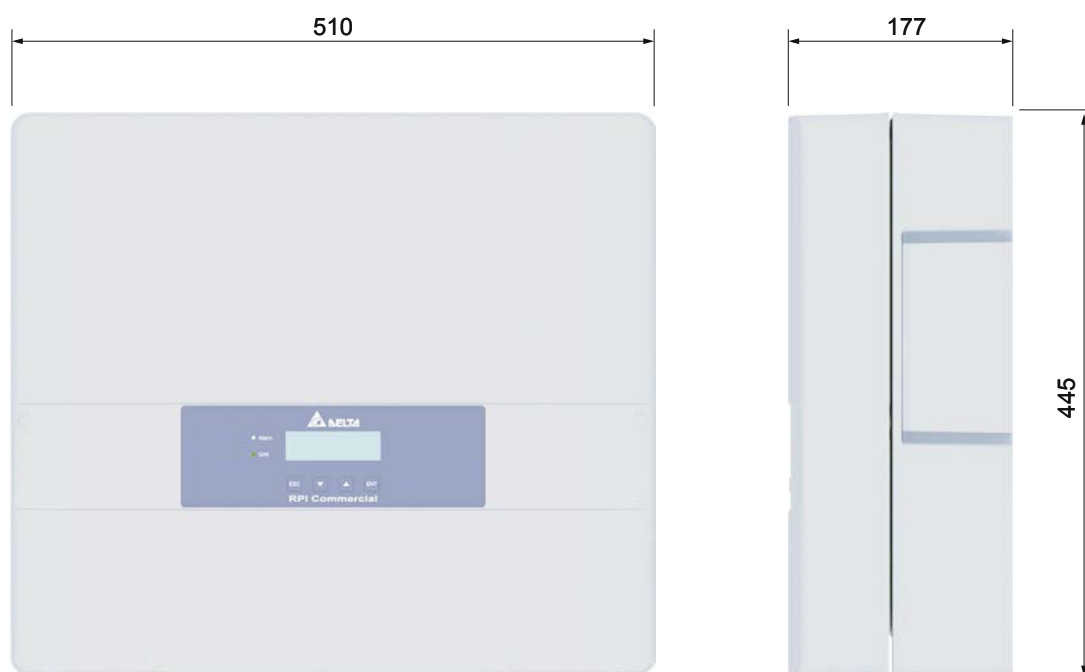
Dimensions de l'onduleur (en mm)
